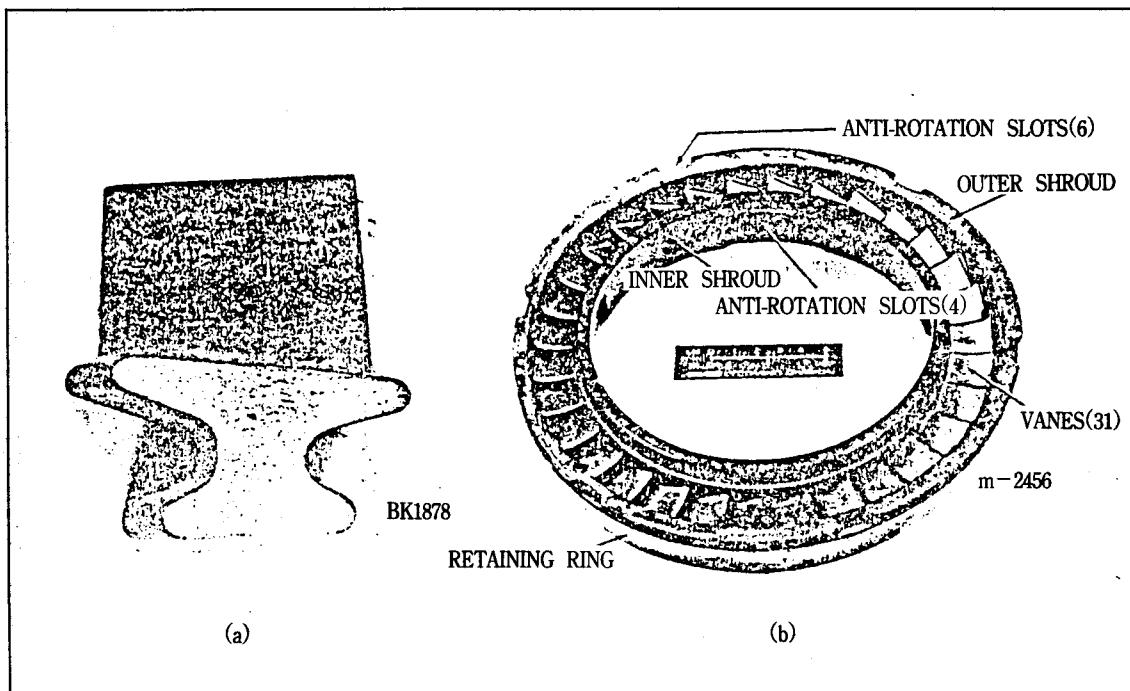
(a) Single blade with circumferential root that is fabricated to net shape, and (b) multipiece ceramic nozzle.
